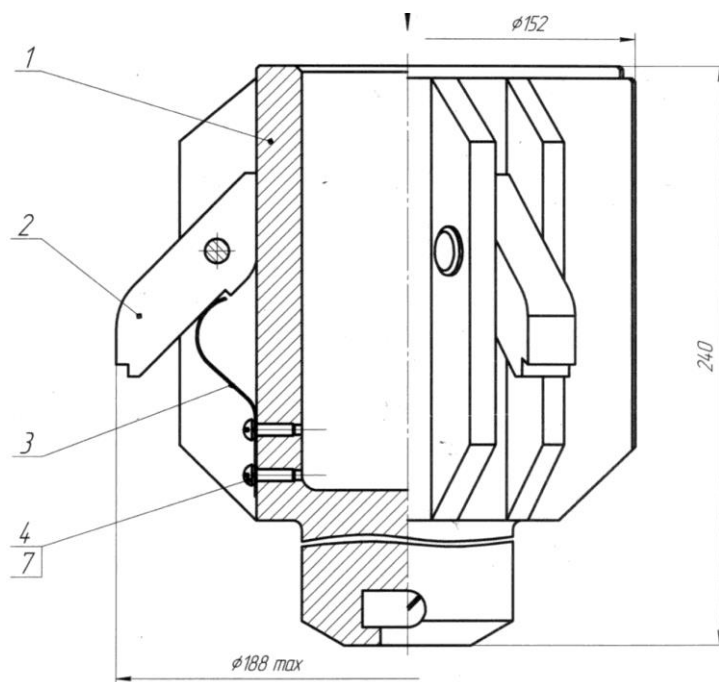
Оправка для випресовування зовнішніх обойм роликопідшипників 7122 та 7224.
